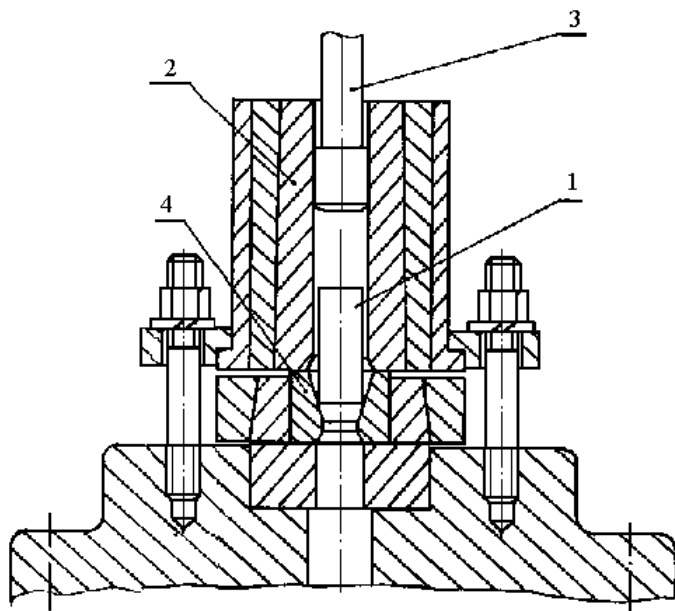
1 – заготовка, 2 – контейнер высокого давления, 3 – пуансон, 4 – матрица.
